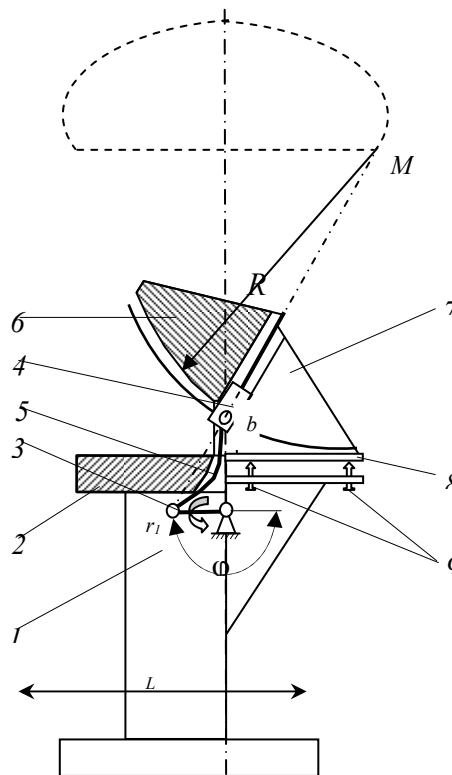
Схема прямолинейно–огibaющего механизма гладильного пресса
